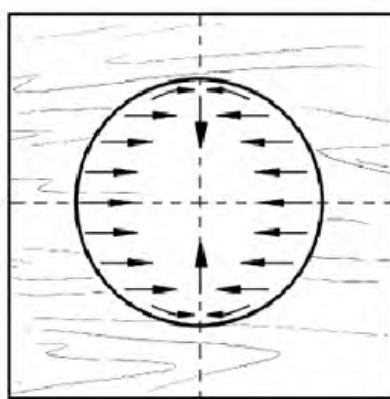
Выполнение резьбы вогнутой выемки на пласти заготовки вторым способом (стрелками показано направление движения инструмента)
